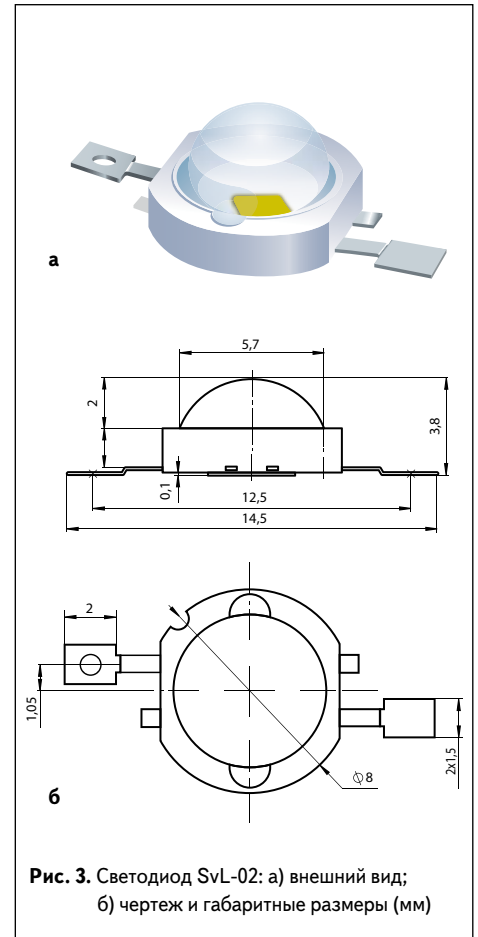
Светодиод SvL-02: а) внешний вид; б) чертеж и габаритные размеры (мм)
